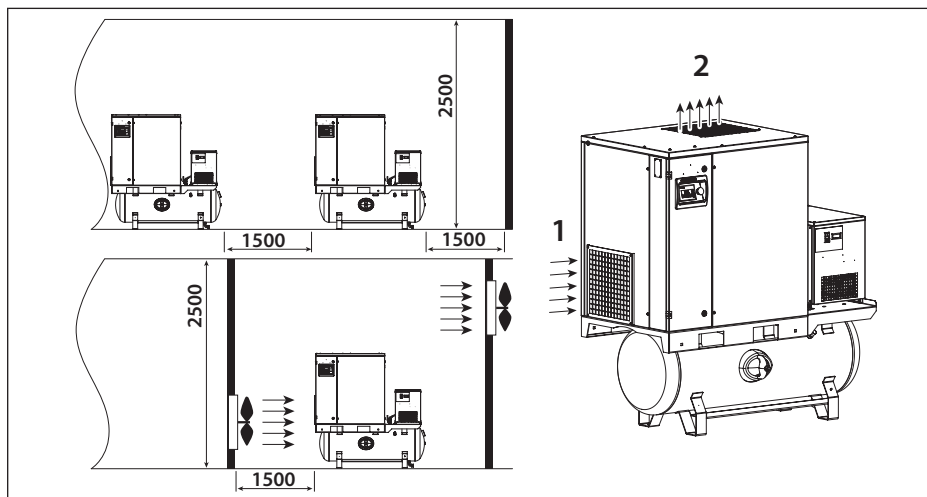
Схема установки компрессора FR07..-FR22, FRD07..-FRD22.
